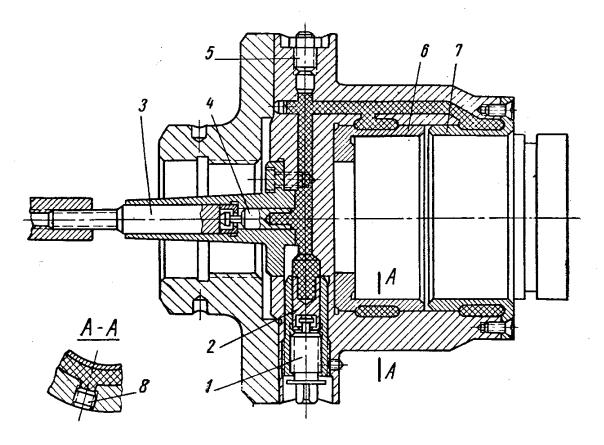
Гидропласмассовое зажимное устройство для закрепления заготовки по наружному диаметру
